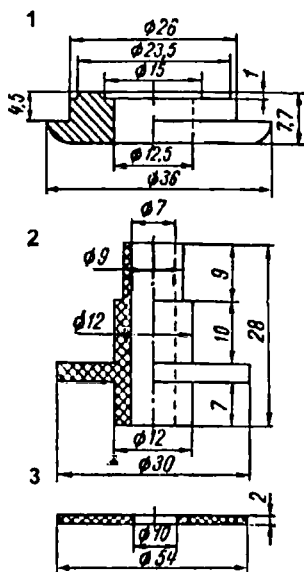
Водяной патрубок, корпус подшипника и диск.
